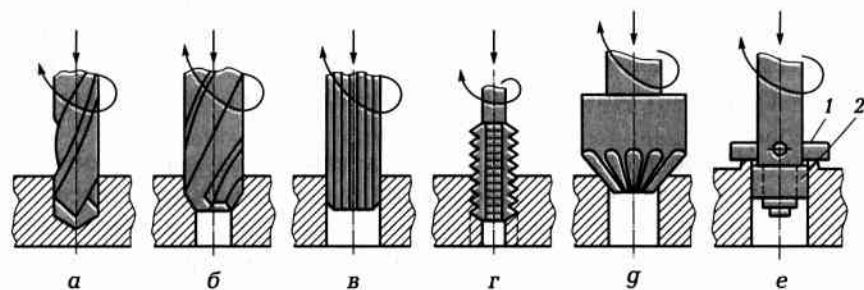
Схемы основных видов обработки, выполняемые на сверлильных станках (а—е)
